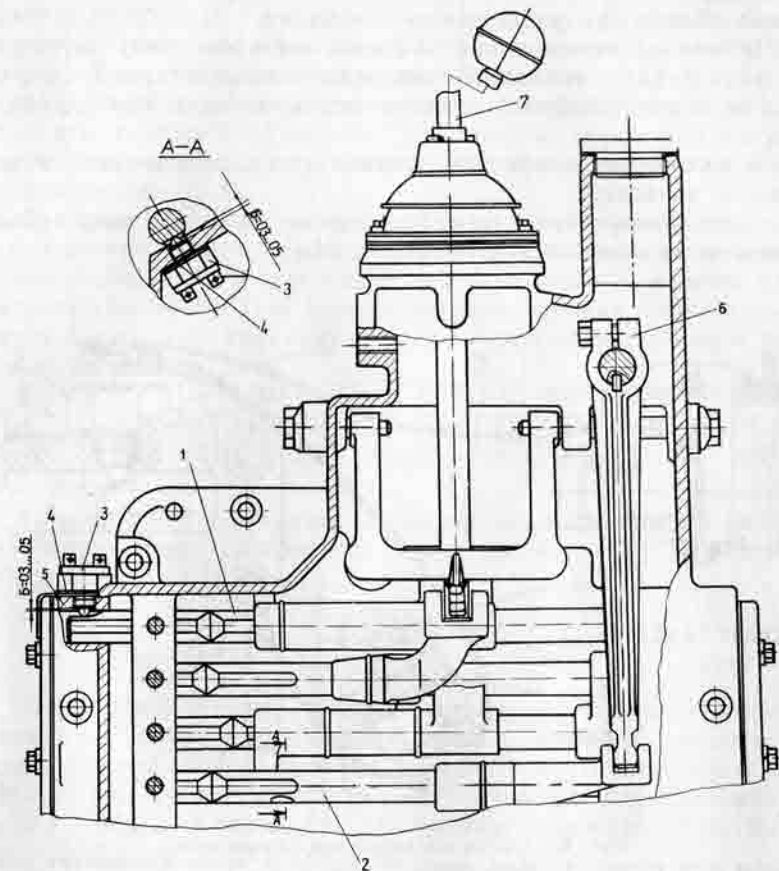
Установка выключателей ВК-403 в механизм переключения передач КПП для блокировки КПП с пусковым двигателем:
